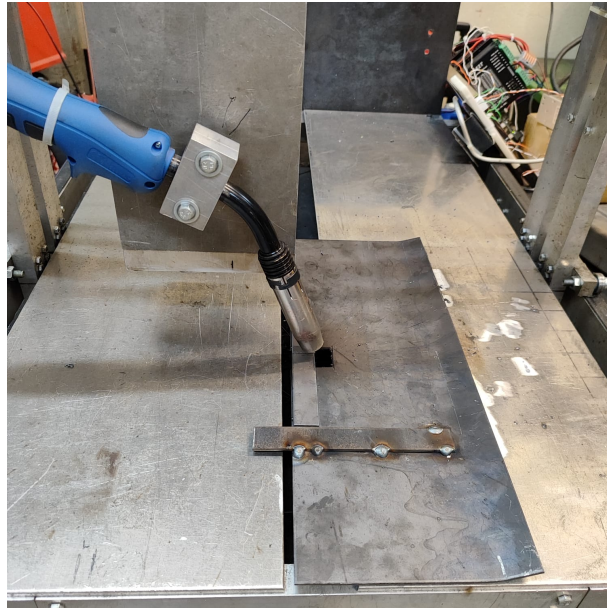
Soldadura na direção X com ângulo de 15° .
